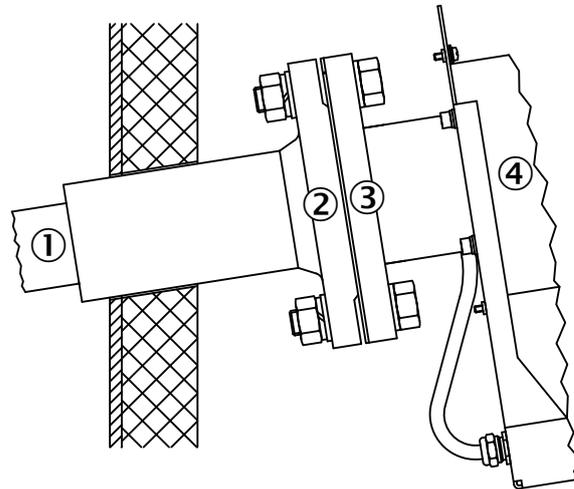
Montage Gasentnehmerrohr an Vorschweißflansch
